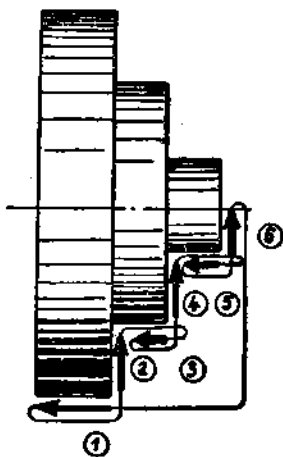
б. Обратный порядок движений резца при обтачивании ступенчатой детали
